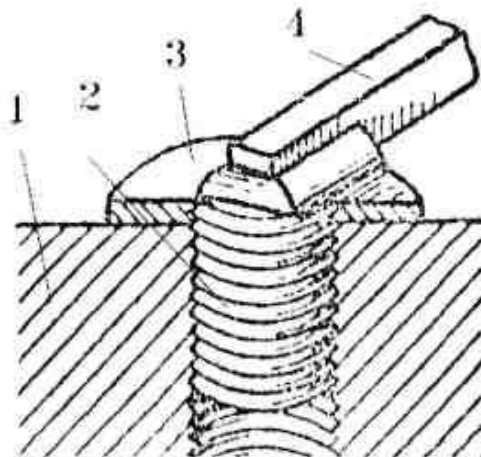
Приварена пластина: 1- деталь; 2- шпилька; 3- пластина; 4- важіль
